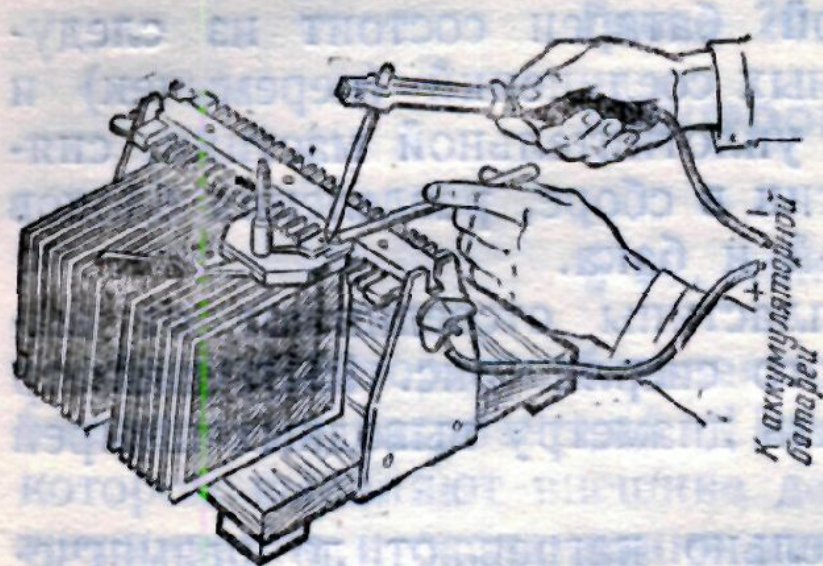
Приспособление для сборки полублока пластин аккумулятора
